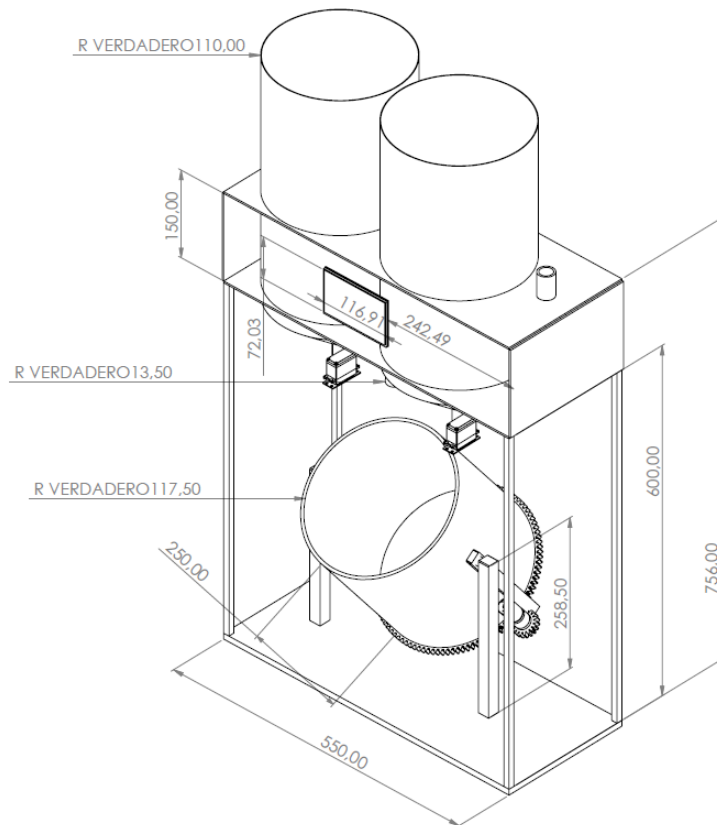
Vista isométrica del prototipo con cotas milimétricas (mm) (propia autoría).
